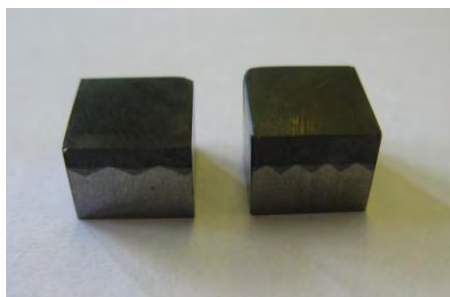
Стандартная вставка оснащенная эльбором-Р (а) и опытные двухслойные пластины (б): 1 –слой КНБ; 2 – твердосплавный субстрат (WC-TaC-Co)-КНБ
